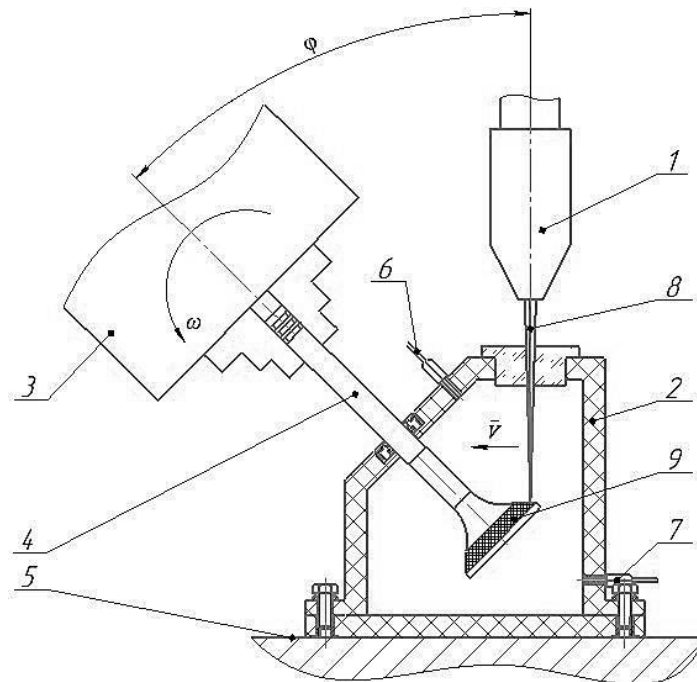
Схема наплавлення зміцнювального покриття: V – вектор швидкості лазерної головки; ω – кутова швидкість обертання трикулачкового патрона; φ – кут нахилу трикулачкового патрона; 1 – лазерна головка; 2 – герметична камера; 3 – трикулачковий патрон; 4 – оброблюваний клапан; 5 – стіл лазерної установки; 6 – випускний патрубок; 7 – впускний патрубок; 8 – лазерний промінь; 9 – присадний порошковий матеріал у вигляді обмазки.
